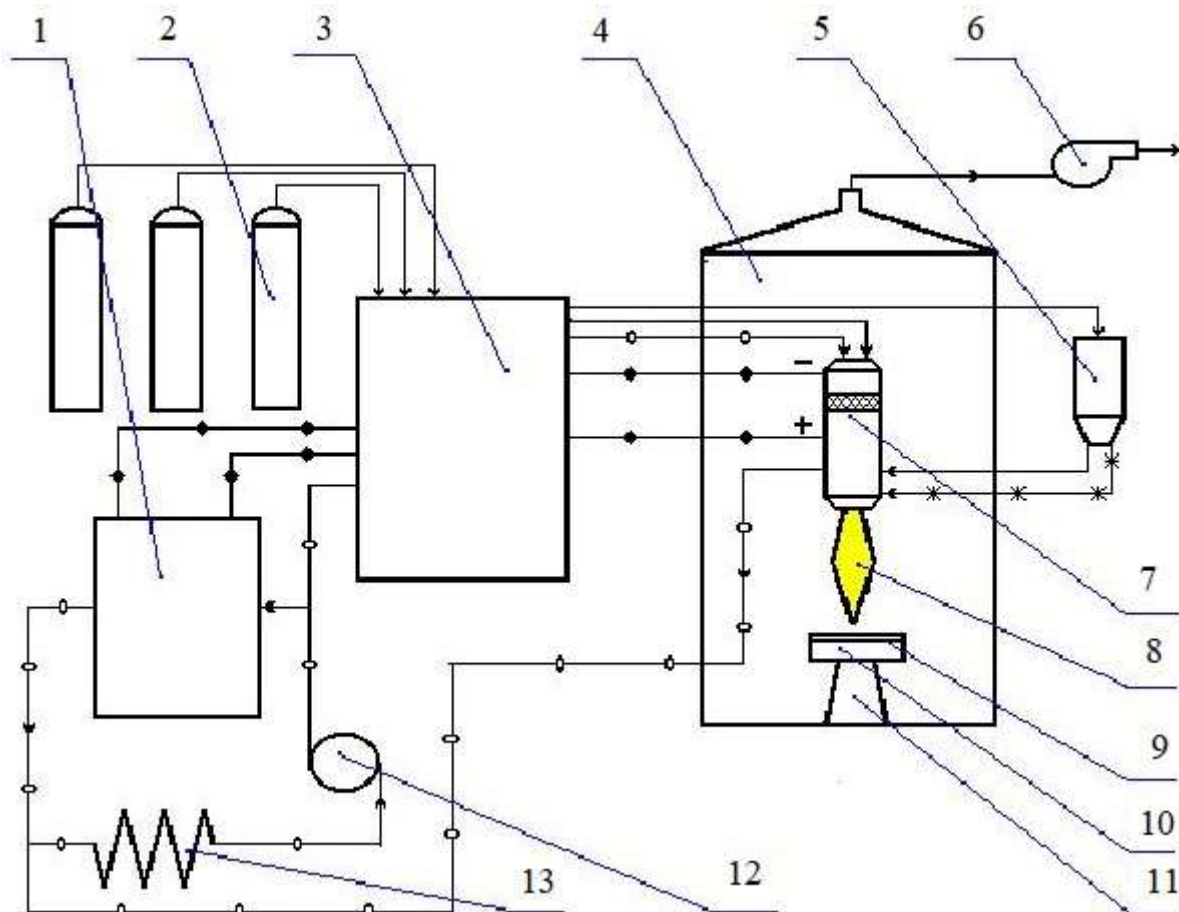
Принципова схема установки УПУ-3Д [8]:
